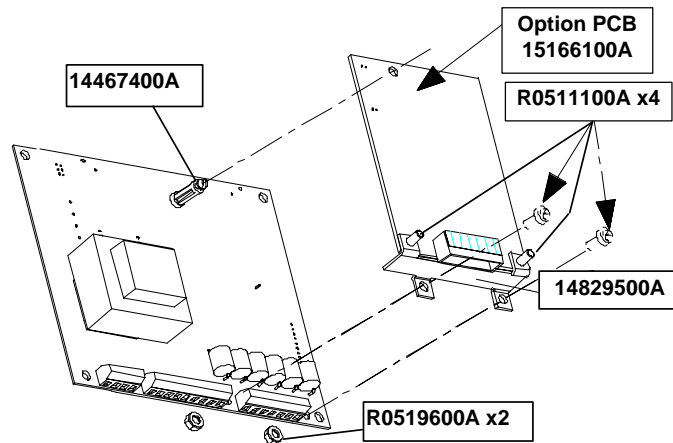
Montando la PCB PROFIBUS opcional en el gabinete de ambientes hostiles
